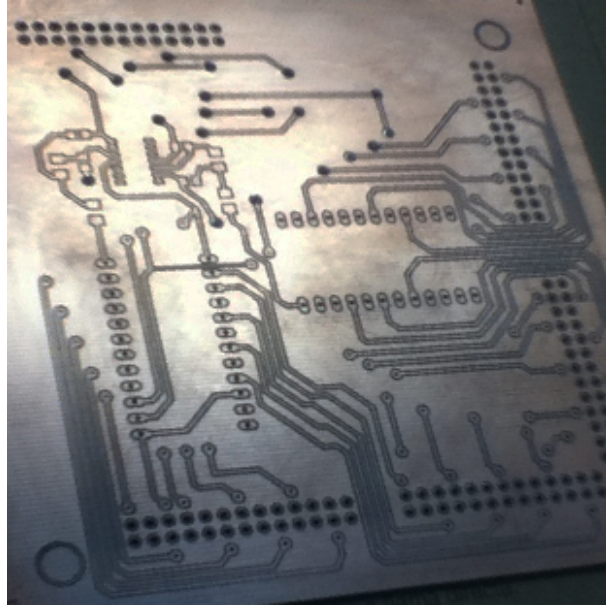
PCB fabricada con AutoLab en el I.I.
